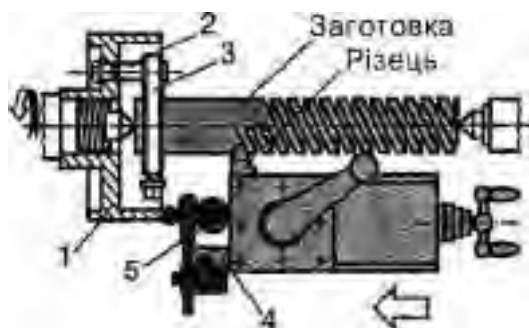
НАРІЗУВАННЯ БАГАТОЗАХІДНОЇ РІЗЬБИ СПОСОБОМ ЗМІЩЕННЯ РІЗЦЯ
